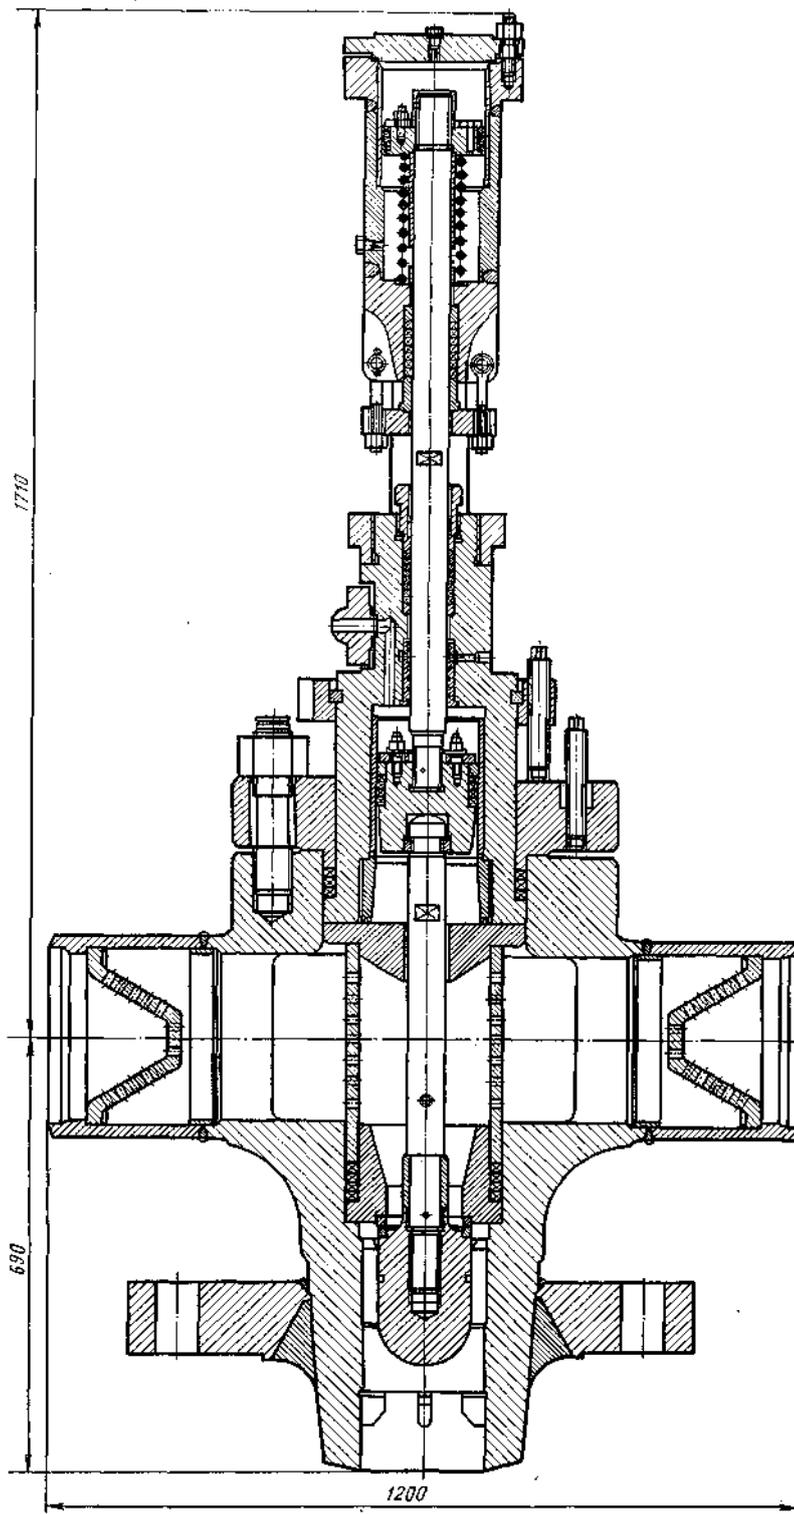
Главный предохранительный клапан 1029-200/250-0
